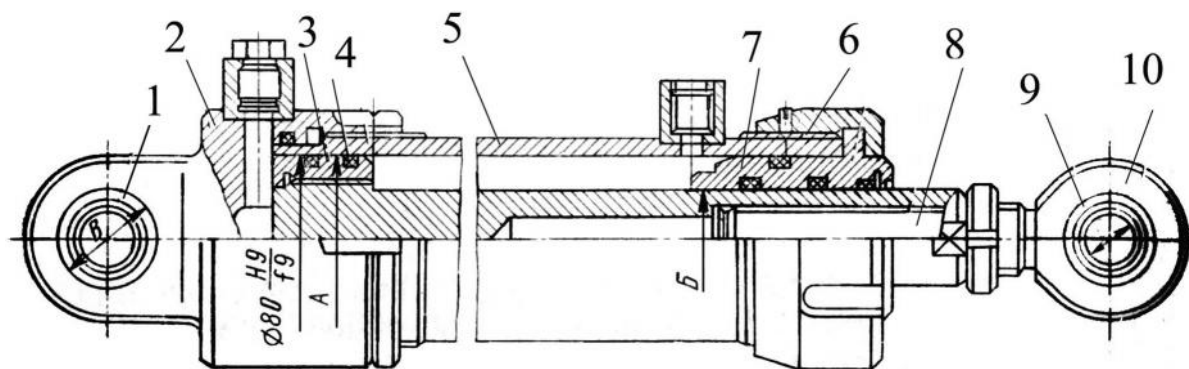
Поршневой гидроцилиндр: 1 – втулка; 2 – крышка нижняя; 3 – поршень; 4 – кольцо резиновое; 5 – цилиндр; 6 – штуцер; 7 – крышка верхняя; 8 – шток; 9 – обойма; 10 – проушина
